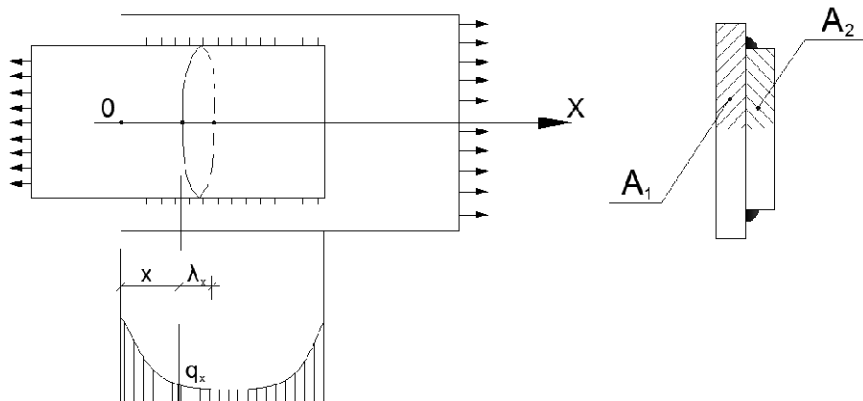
Расчетная схема сварного соединения с фланговыми швами [38; 39]
